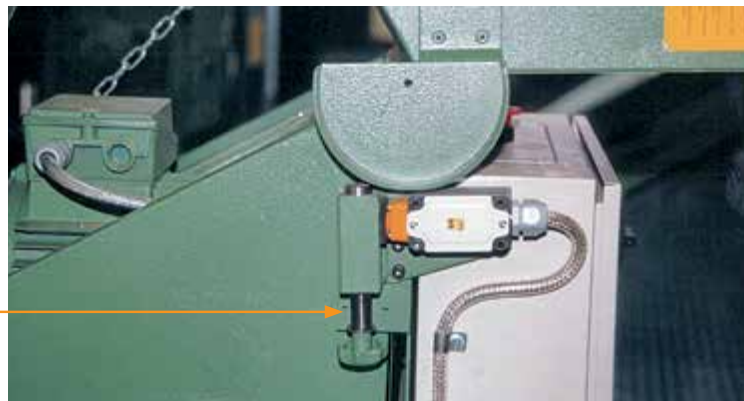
Schwer manipulierbare mechanische Nachlaufüberbrückung in Form einer Spindel: Schutzeinrichtung geöffnet
